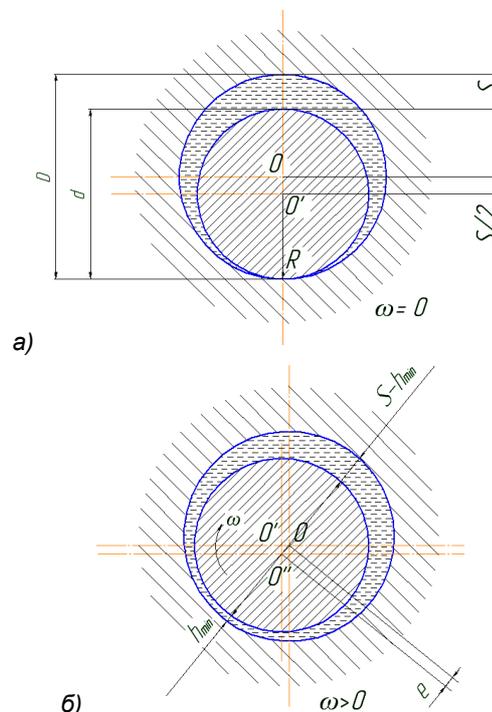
Положение шейки коленчатого вала во вкладыше подшипника скольжения: а – в состоянии покоя; б – в рабочем положении
